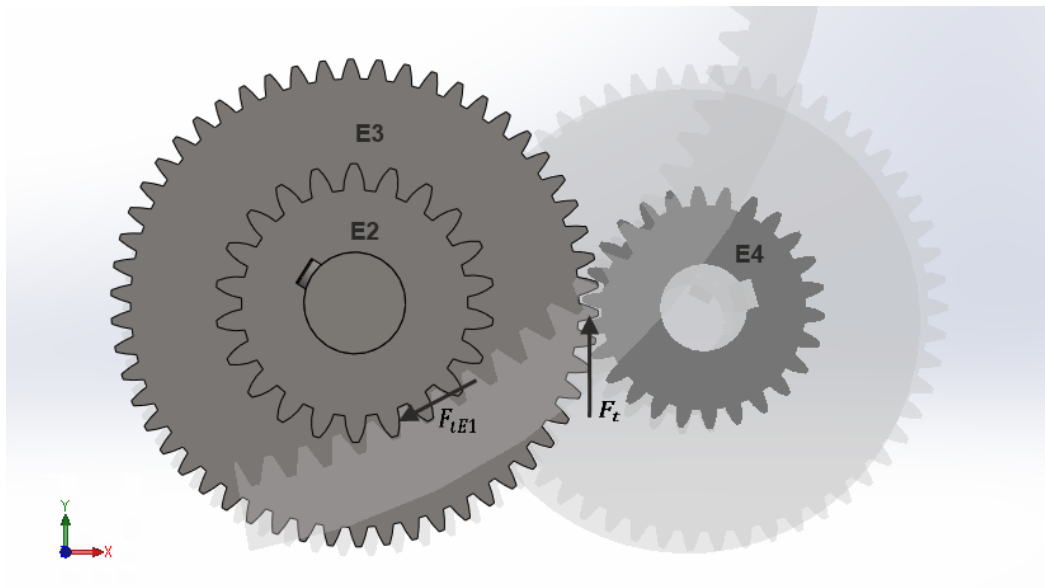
Fuerzas actuantes en el engranaje E2, engranaje E3 y engranaje E4. Fuente: Elaboración propia.
